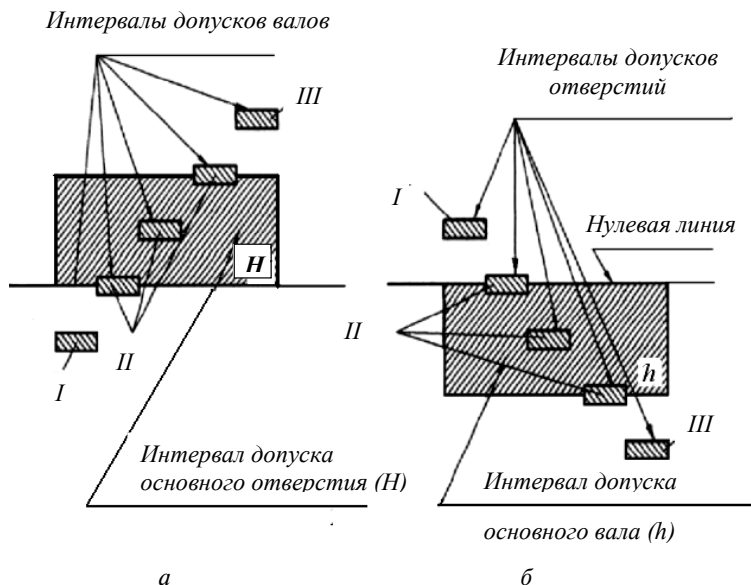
Схема расположения интервалов допусков посадок в системе вала и в системе отверстия: *а* — система отверстия; *б* — система вала; I — интервалы допусков посадок с зазором; II — интервалы допусков переходных посадок; III — интервалы допусков посадок с натягом
